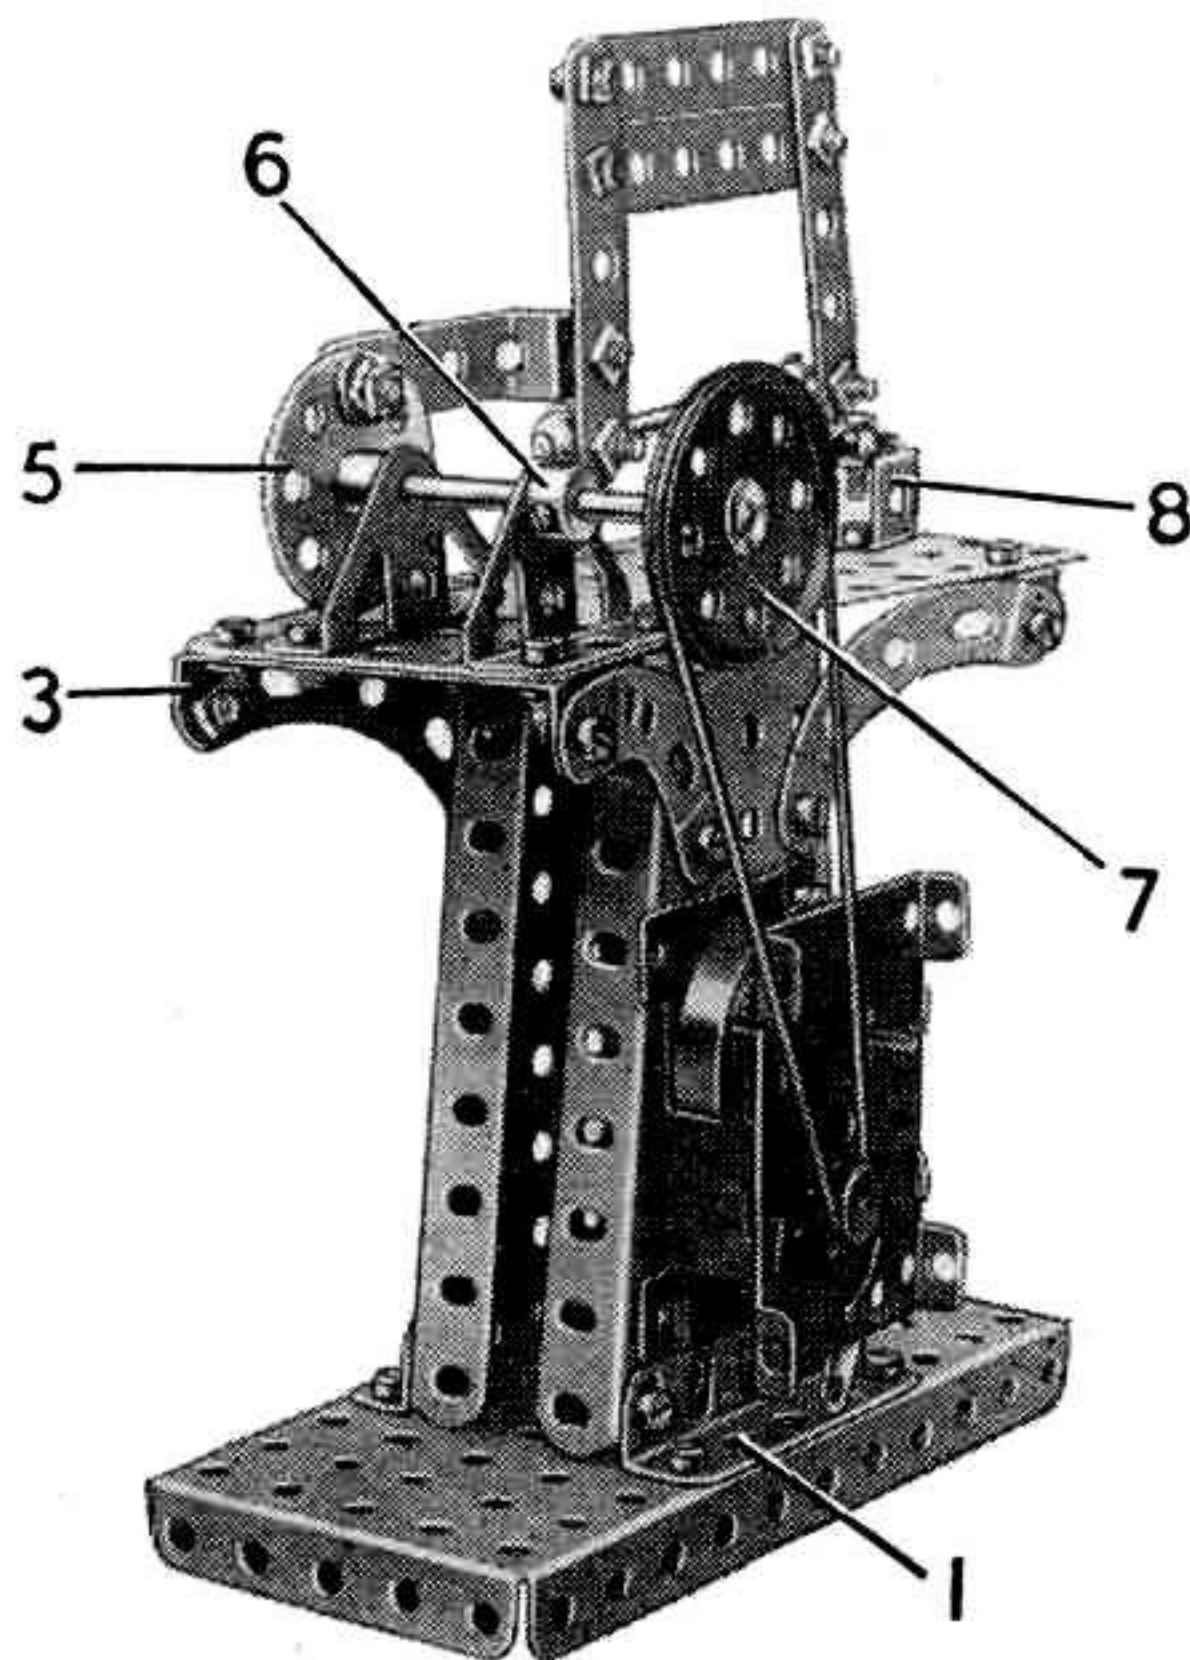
La scie à métaux vue de l'arrière avec la disposition du moteur et de l'entraînement.
